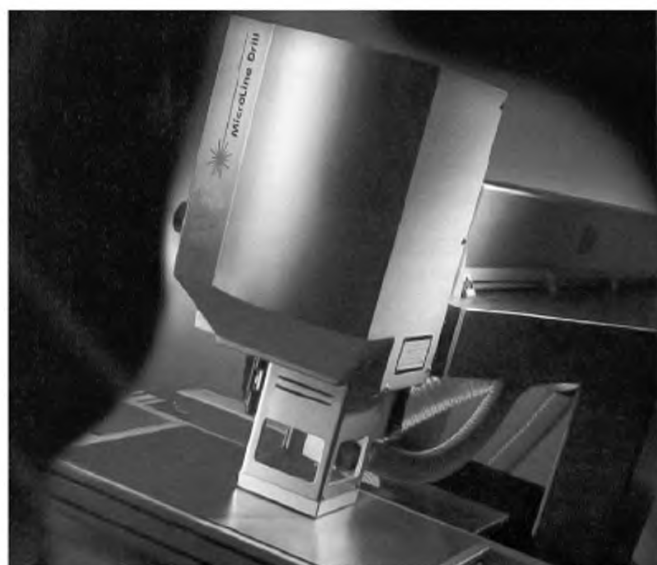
PCNC — станок для лазерной обработки деталей
